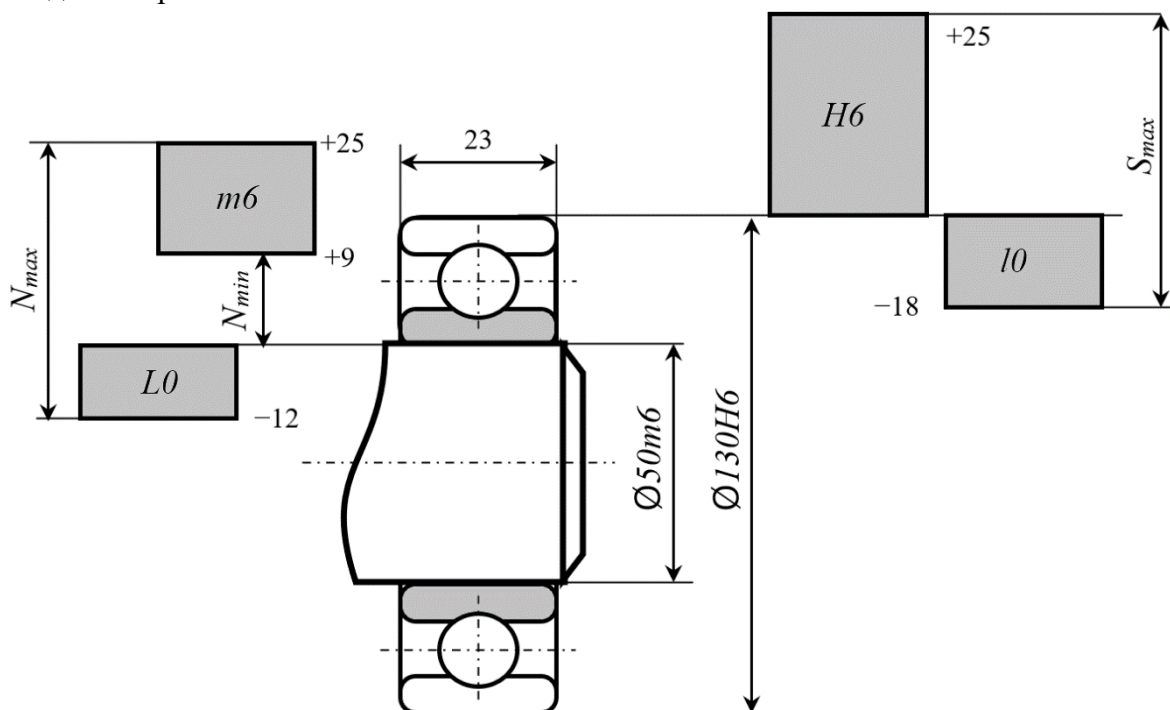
Схема розташування полів допусків підшипника і позначення підшипникових посадок на кресленні.
